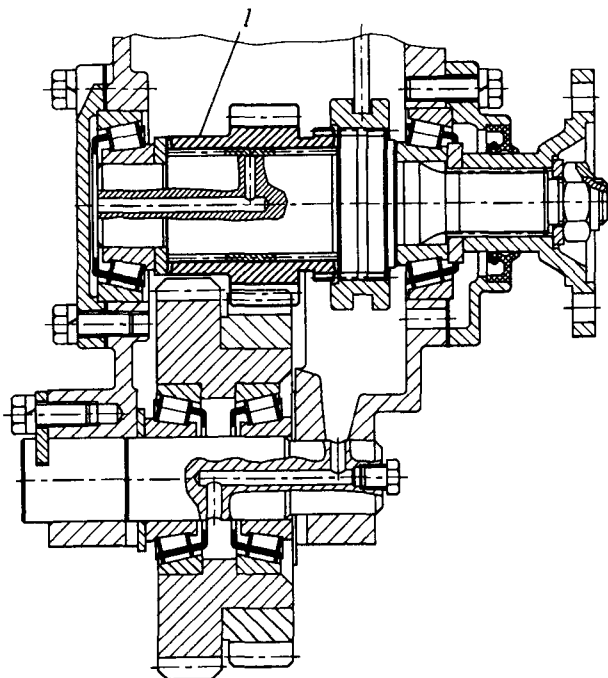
Фрагмент сборочного чертежа коробки отбора мощности
